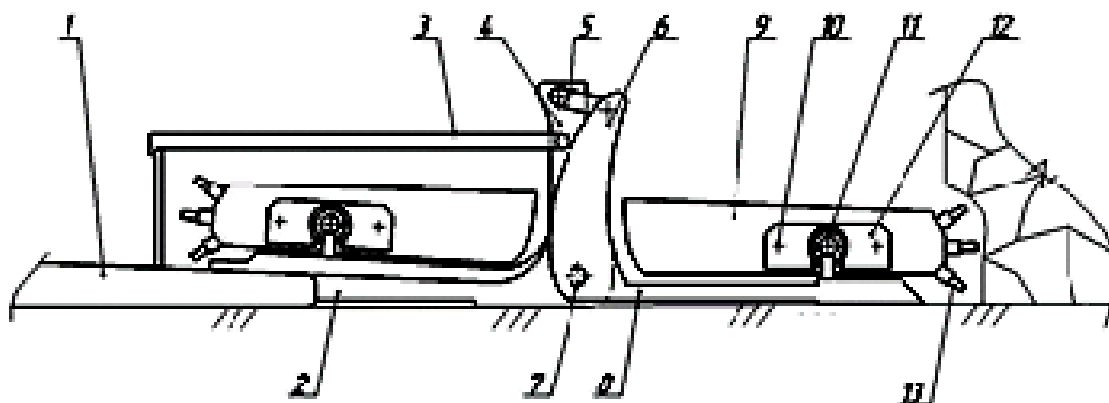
Забойный зарубной скребковый конвейер: 1 – основания секции крепи; 2 – заваль- ные решетки; 3 – опорный лист; 4 – опорная стойка; 5 – гидродомкрат; 6 – опорный рычаг забойного решета; 7 – опорная цапфа; 8 – забойный решета; 9 – скребок; 10 – тяговые цепи; 11 – опорная направляющая; 12 – скользящая каретка; 13 – резцы.
